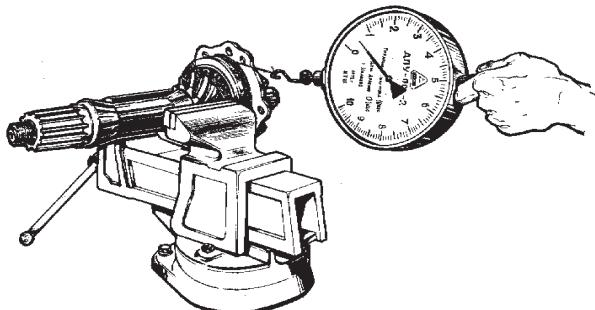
Проверка регулировки подшипников ведущей конической шестерни
